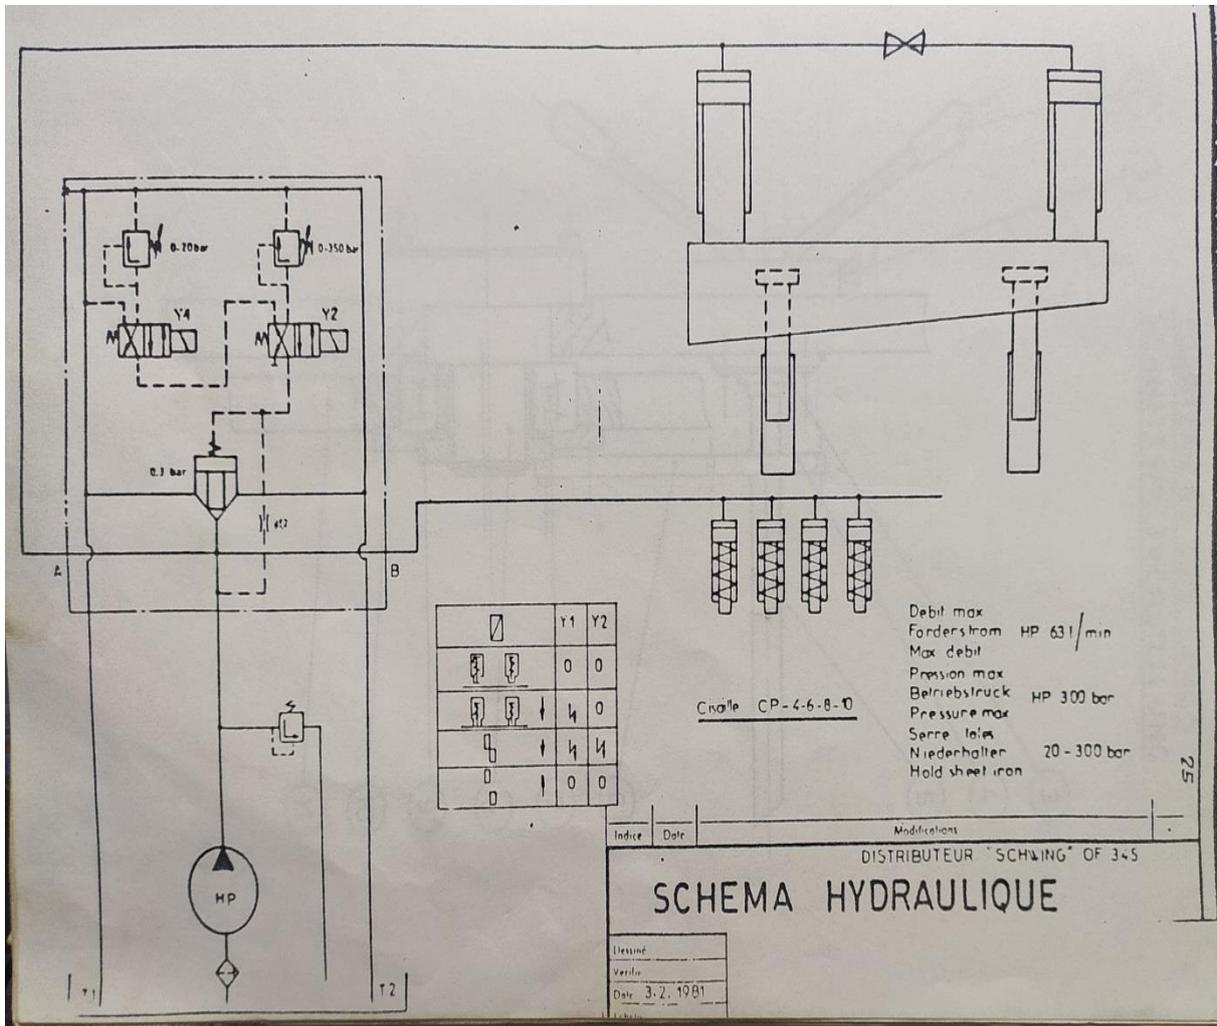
Schéma hydraulique de la machine S'AGITA [17]
